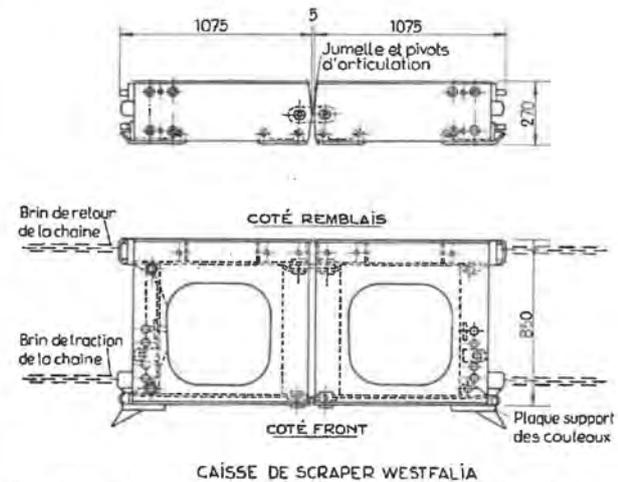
Caisse de scraper à deux éléments, le brin de retour de la chaîne passe dans un tube guide situé sur la paroi arrière de la caisse.
